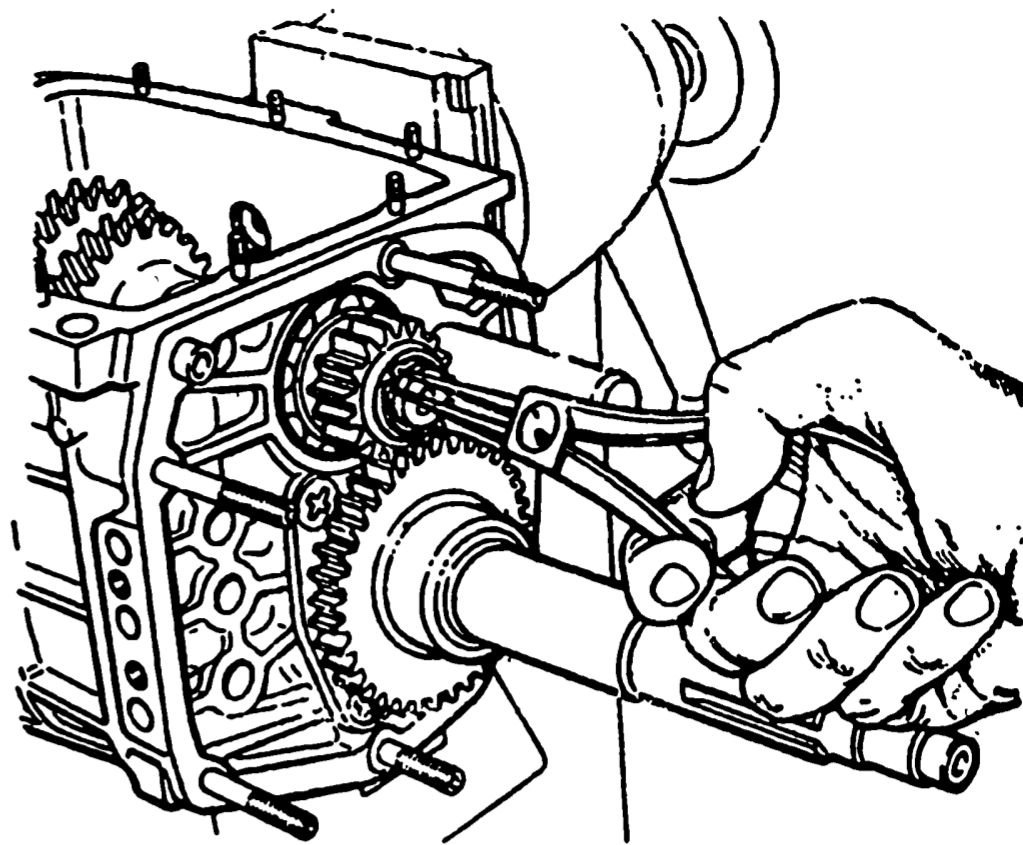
Снятие стопорного пружинного кольца шестерни заднего хода с промежуточного вала
